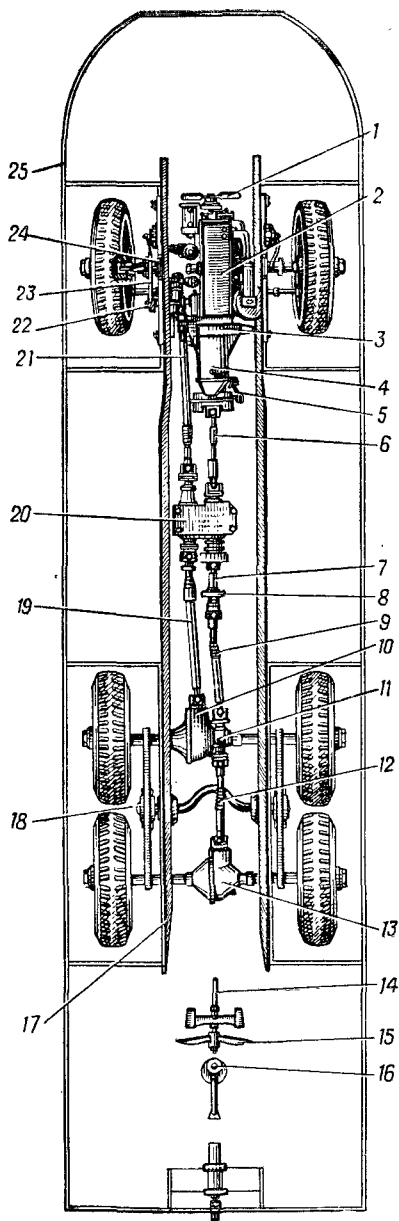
Схема расположения основных агрегатов плавающего трехосного автомобиля БАВ:
